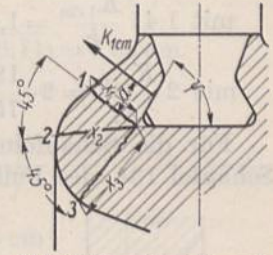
Zur Berechnung von Turbinenradkränzen.
